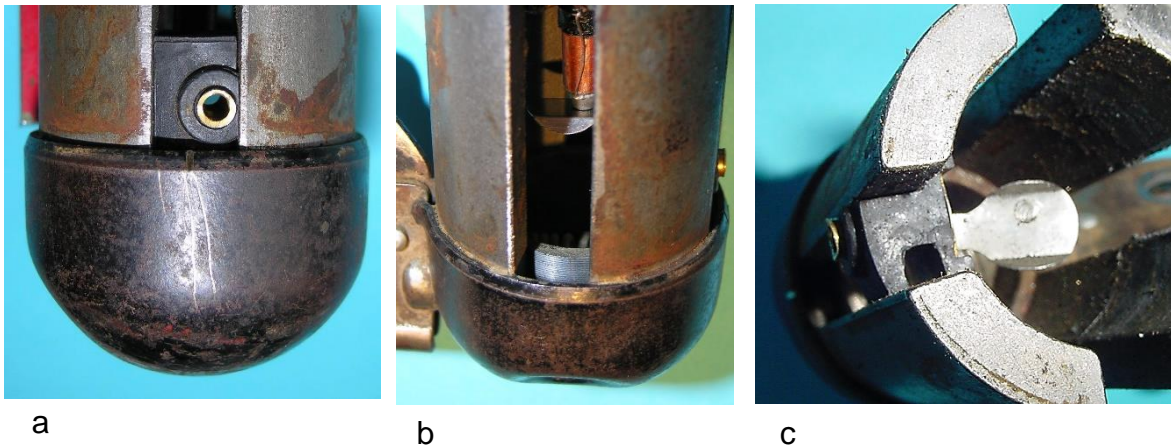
Kontaktfeder: a) Gewindestück mit Grundkörper für den Kabelanschlussbolzen, b) Kontakt des Ankers mit der Blattfeder, c) Grundkörper mit der Blattfeder
